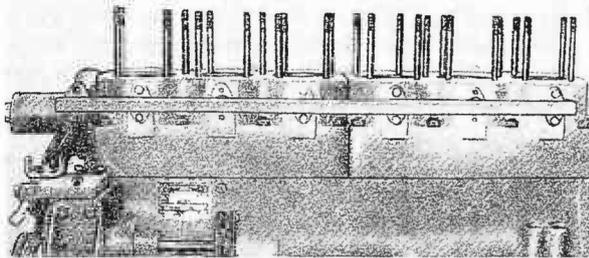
Ausrichten der Zylinderblöcke sowie der Kühlmittelpumpe
